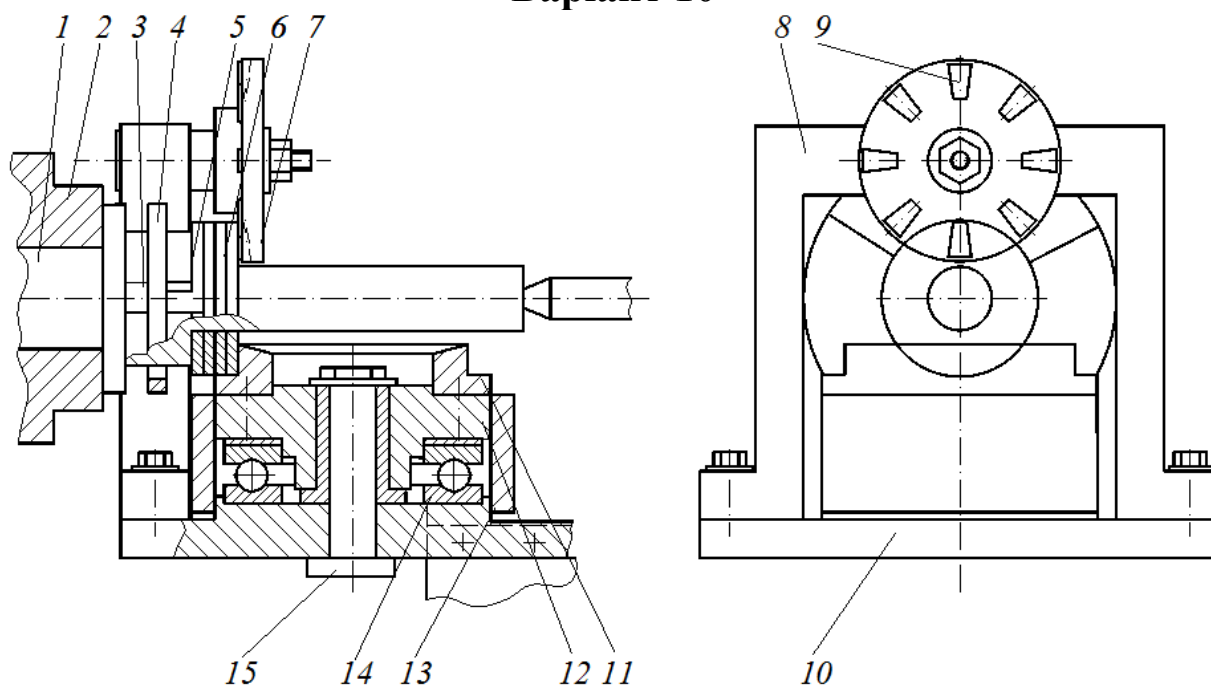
Пристрій для виготовлення гвинтової заготовки способом навивання смугової заготовки ребром на оправу: 1 – ступінчаста циліндрична оправу, 2 – патрон токарного верстату, 3 – осьовий паз на більшій ступені оправу, 4 – втулка, 5 – торець оправу, виконаний один гвинтовий виток з кроком, що дорівнює товщині спіралі, 6 – зігнутий кінець стрічки, 7 – обтискний ролик, 8 – кронштейн, 9 – конічні ролики, 10 – механізм подачі верстату, 11 – формотворний ролик, 12 – корпус, 13 – кожух, 14 – упорний підшипник, 15 – вісь.
